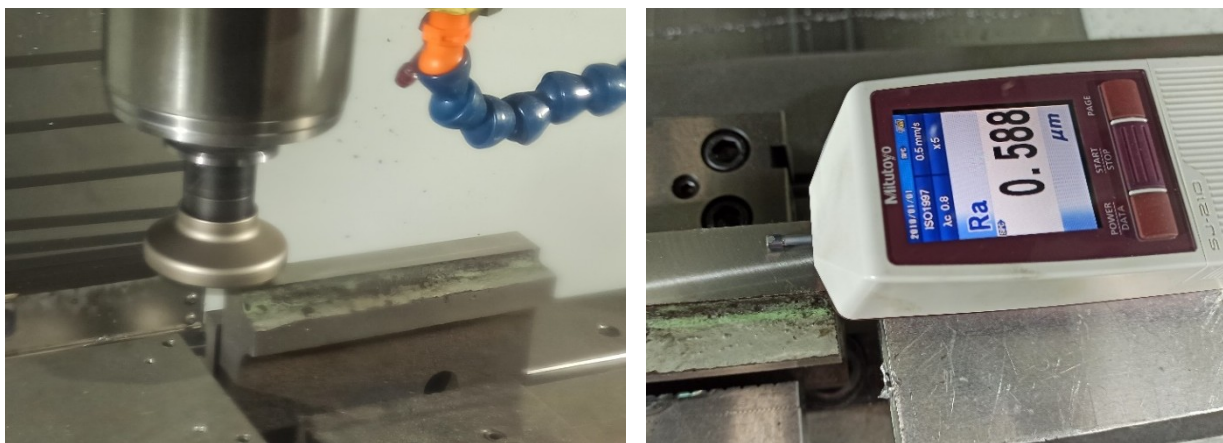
Процесс обработки заготовки и проведение измерения шероховатости поверхности данной заготовки профилометром Mitutoyo SJ-210
